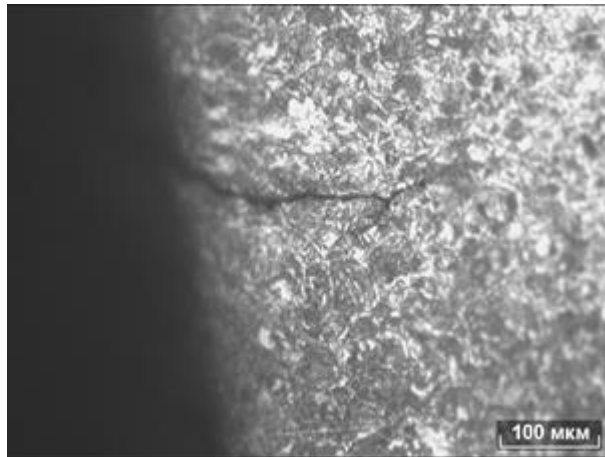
Микротрещины, распространяющиеся от излома сварного шва по металлу подкладки
